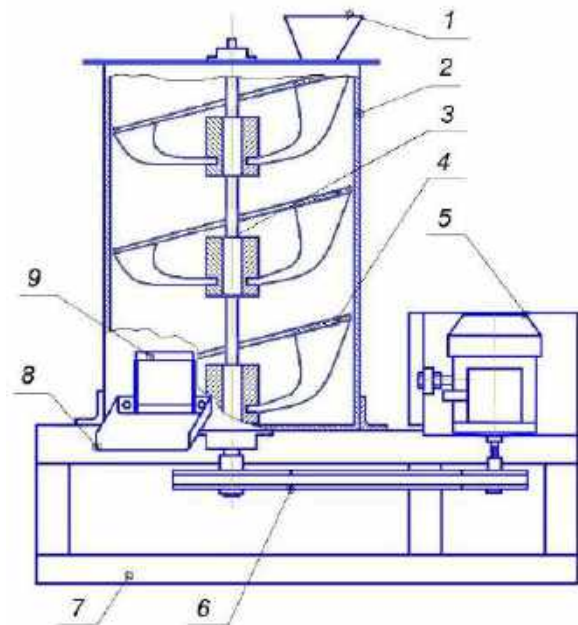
Схема та загальний вигляд лабораторного змішувача:
